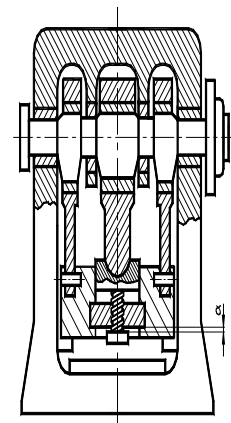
Конструкція кривошипного преса для штампування з крученням
